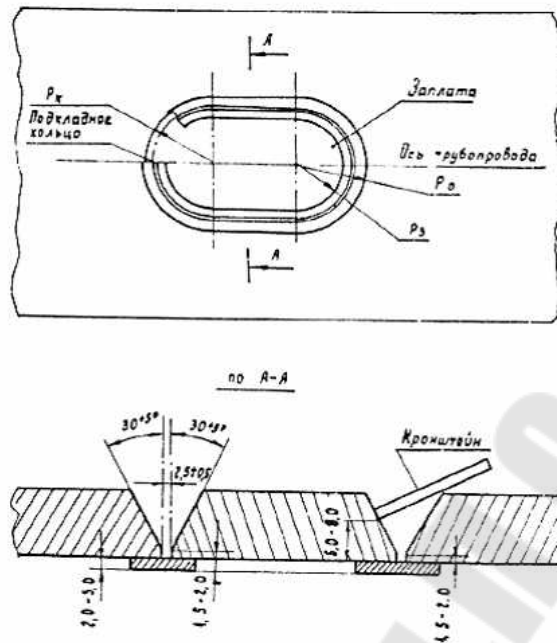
Форма и ориентация отверстия, заплата и подкладного кольца и схема разделки кромок под сварку:
